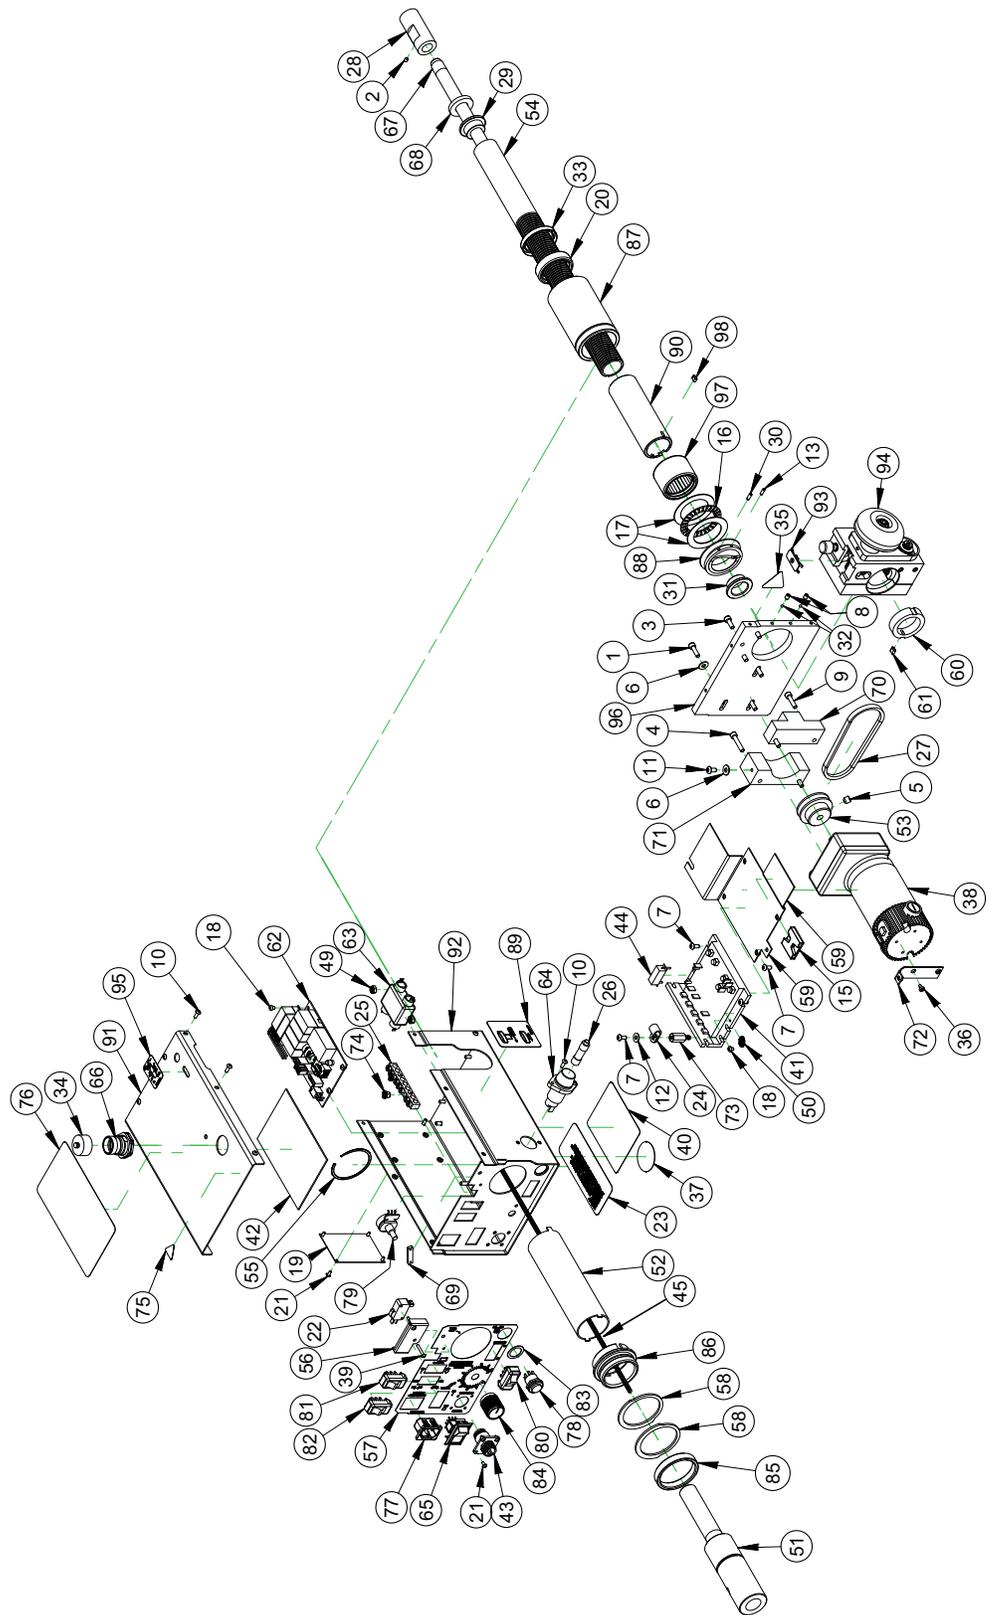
CONJUNTO DE LA BW2600 (N/P 91579)
